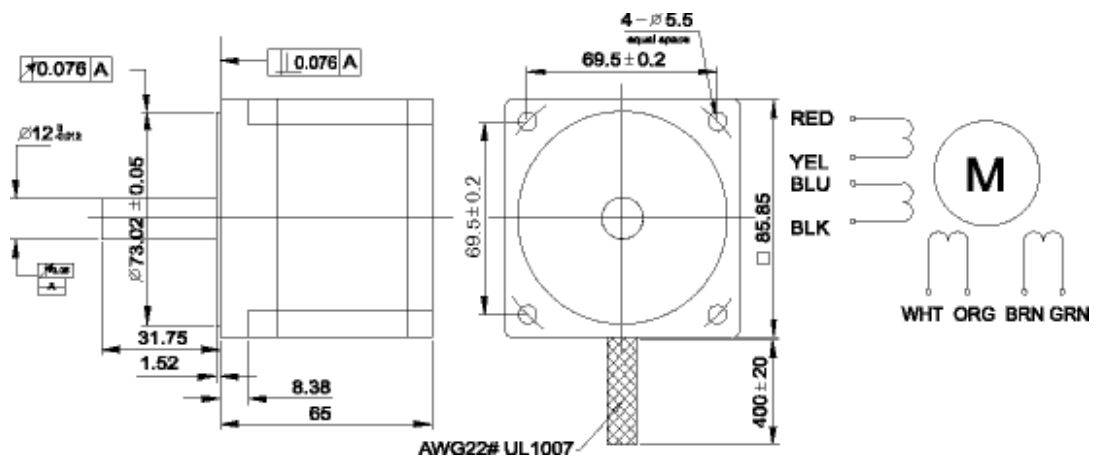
Габаритні розміри крокового двигуна
